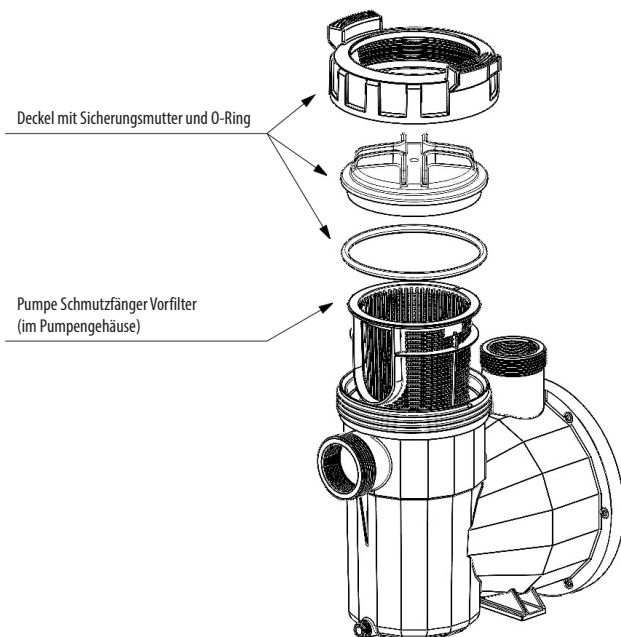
EXPLOSIONSZEICHNUNG DER PUMPENBAUGRUPPE
